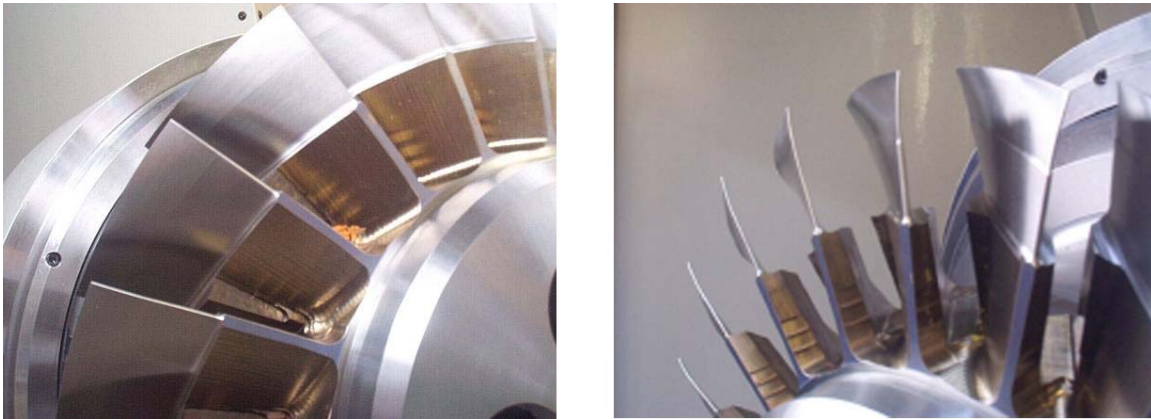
Лопатки осевого колеса компрессора ГТД (пример защемленной пластины сложной формы)
